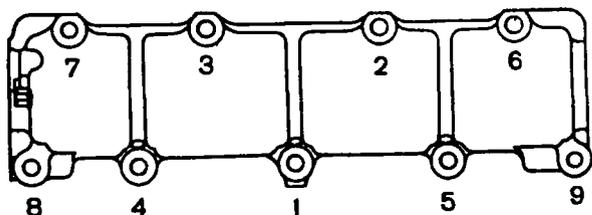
Порядок затягивания гаек корпуса подшипников распределительного вала
